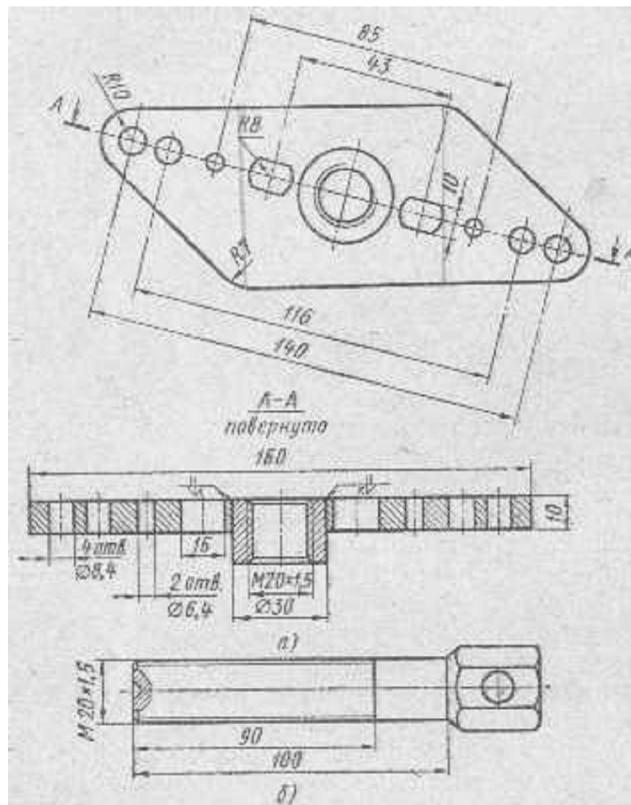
Универсальное приспособление для разъединения половин картера, выпрессовки и запрессовки подшипников:
